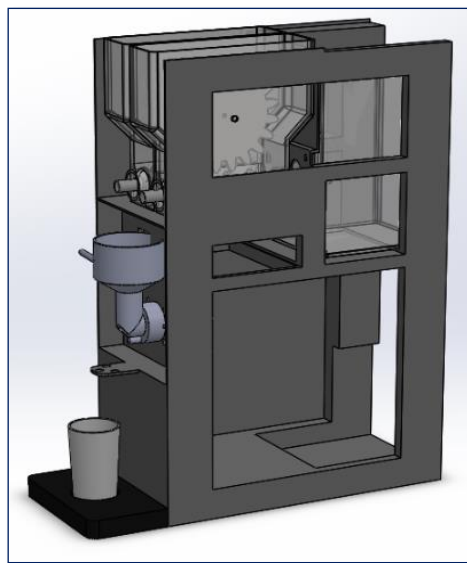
9. Ubicación en máquina del motor CT12120-36ZY. Fuente: Autoría propia.
